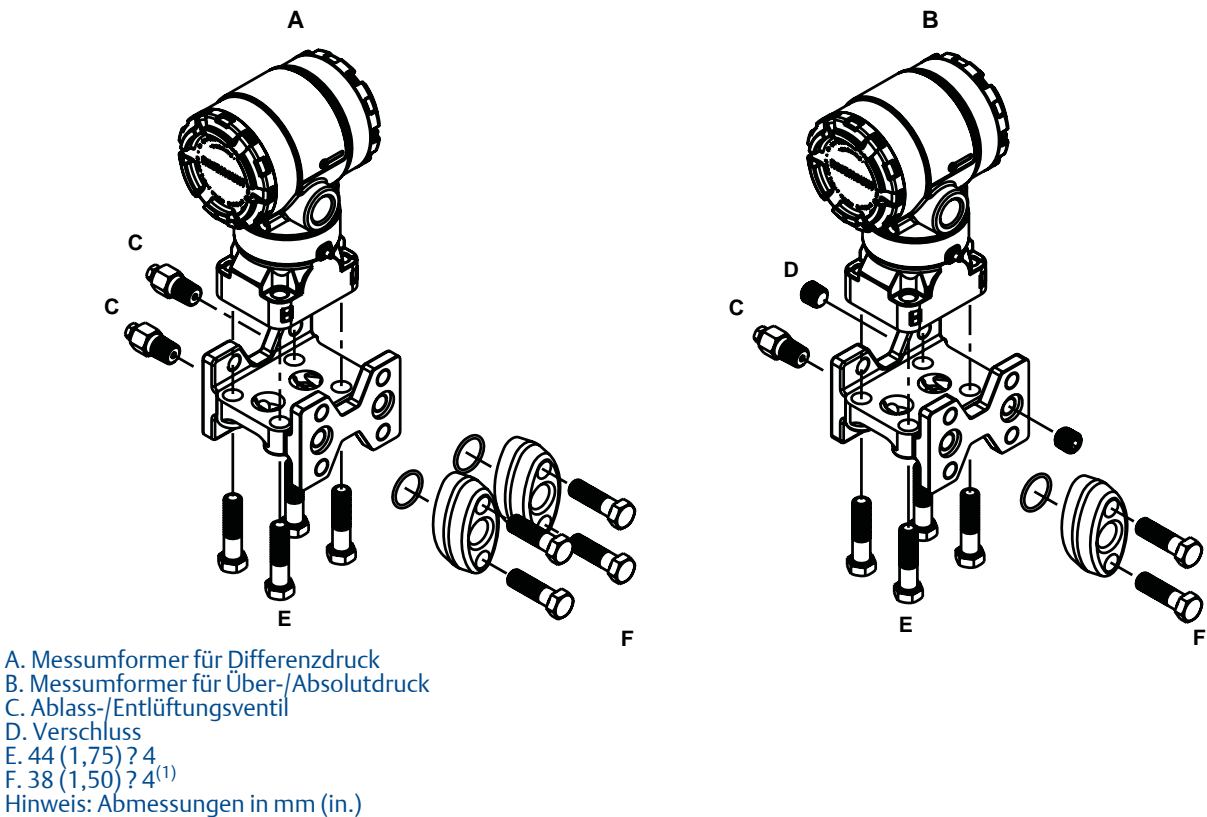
Montageschrauben und -anordnung für den Coplanar Flansch
